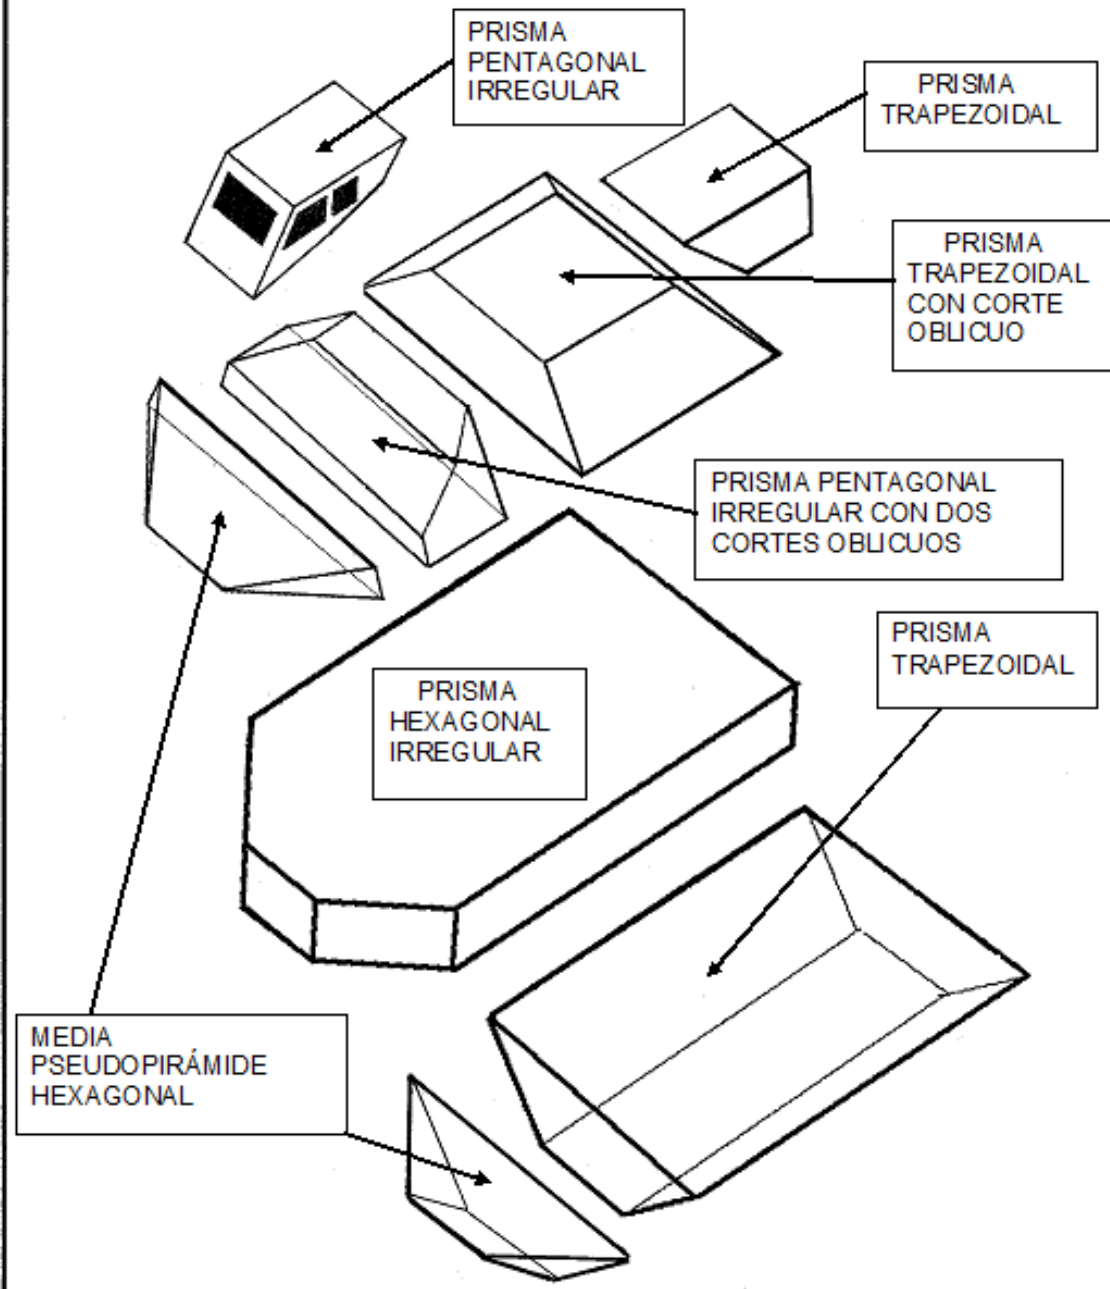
Práctica 57 Tractor Artic Explorer, vista explosionada B
